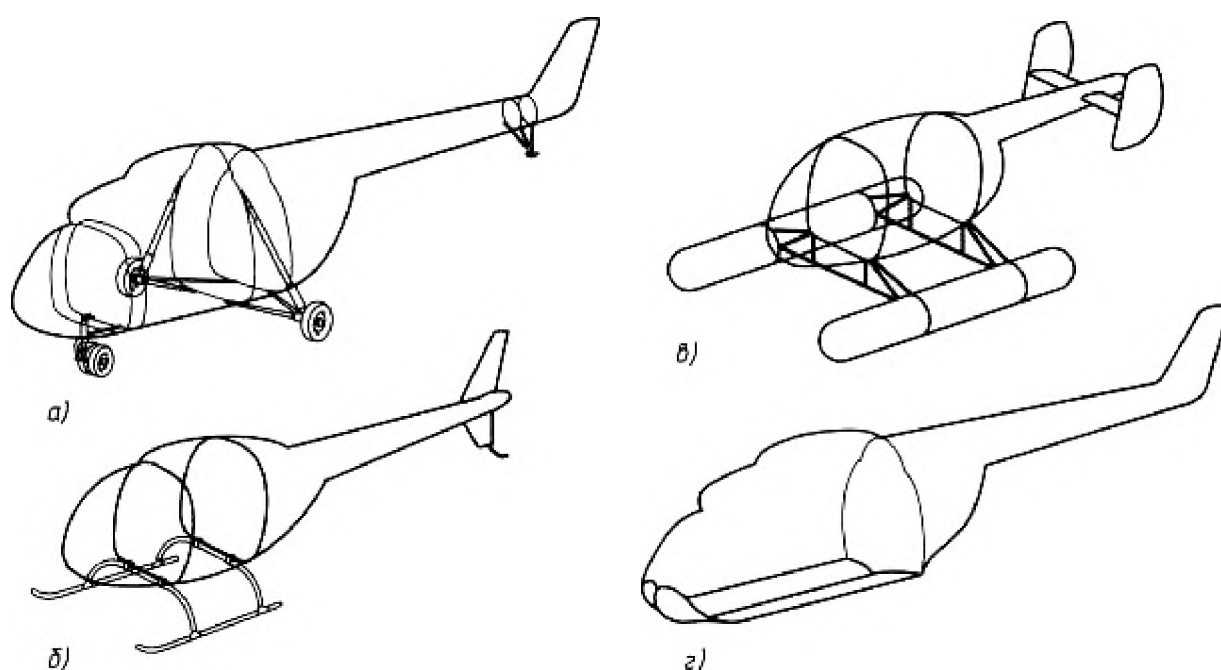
Типы шасси [14]: а- колесное; б- полозковое; в- поплавковое; г-лодка.
